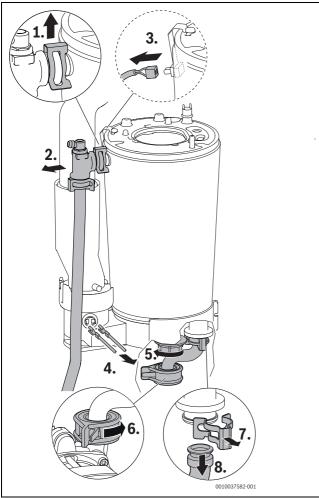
Détacher le tube de départ, retirer le câble et détacher le tube retour
